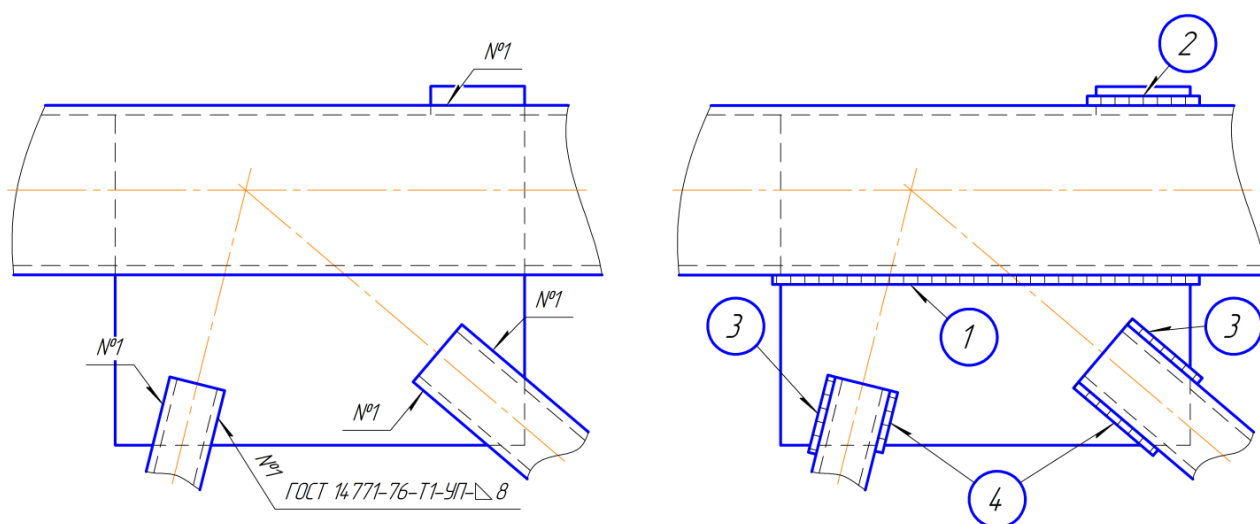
Последовательность наложения сварных швов узла верхнего пояса фермы
